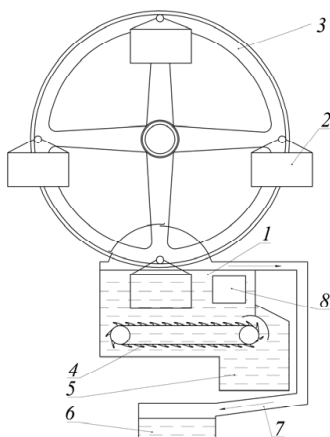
Схема погружной моечной машины: 1 – ванна с моечным раствором; 2 – контейнер для размещения деталей; 3 – роторное колесо; 4 – шнековое устройство для очистки ванны от механических загрязнений; 5 – отстойник; 6 – резервуар для сбора маслянистых загрязнений; 7 – устройство для очистки раствора от маслянистых загрязнений; 8 – термоэлектрический нагреватель
